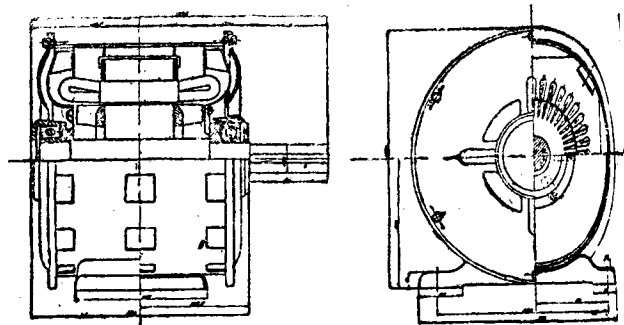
Общий вид пробного двигателя 4,5 kW, 1 500 об/мин со сварной вентиляцией.
